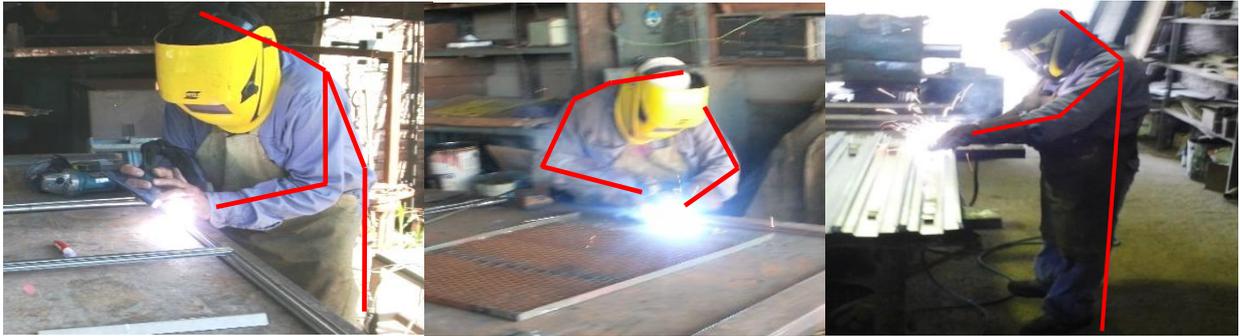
Estudio Ergonómico en Soldadura
